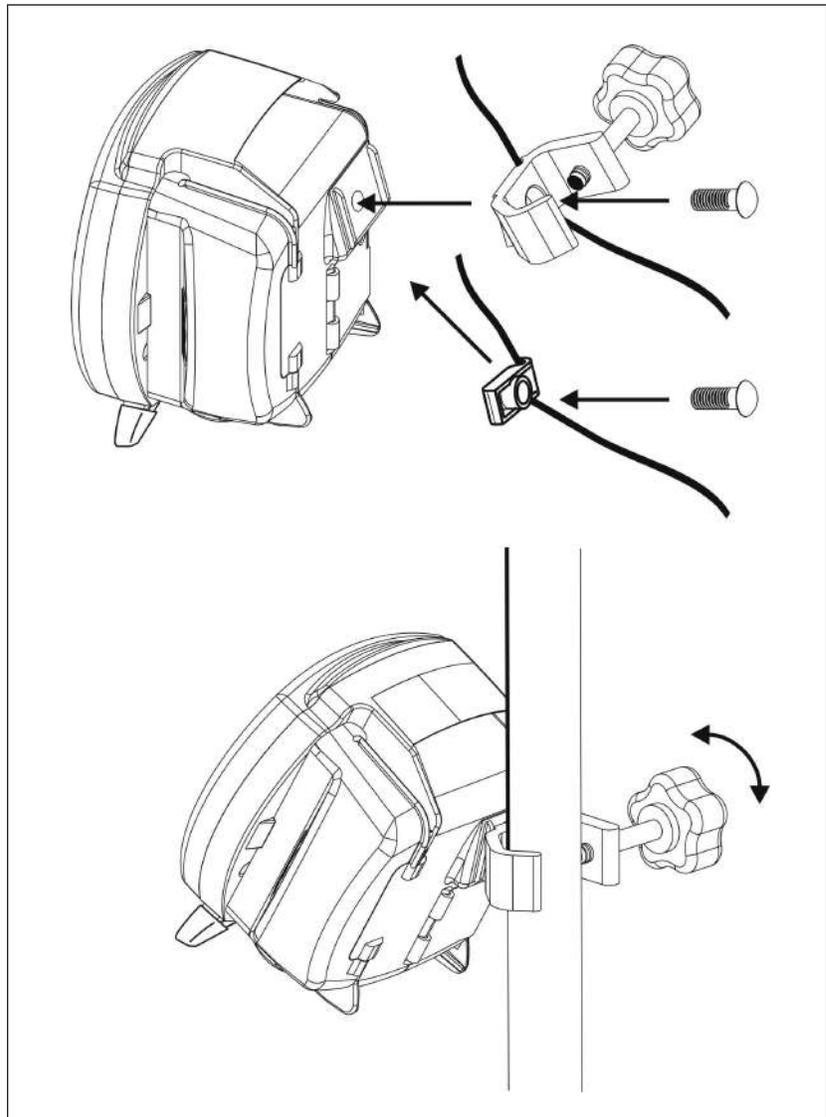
Ligar e utilizar o clampe para montagem em suporte ou o clipe do cabo.
